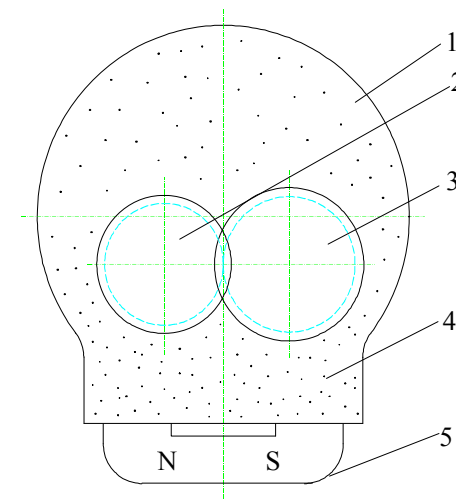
Схема экспериментального редуктора Р-1 с магнитом и магнитоактивной смазкой: 1 – корпус; 2 – блок-шестерня; 3 – шестерни; 4 – магнитоактивная смазка; 5 – магнит
